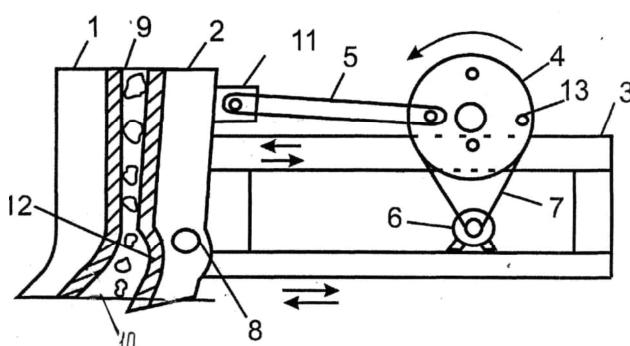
Щековая дробилка двойного дробления: 1 – неподвижная щека; 2 – подвижная щека; 3 – рама; 4 – маховик; 5 – шатун; 6 – электродвигатель; 7 – клиновый ремень; 8 – ось установки подвижной щеки; 9 – загрузочное отверстие; 10 – разгрузочное отверстие; 11 – проушина; 12 – углубление; 13 – отверстие в маховике
